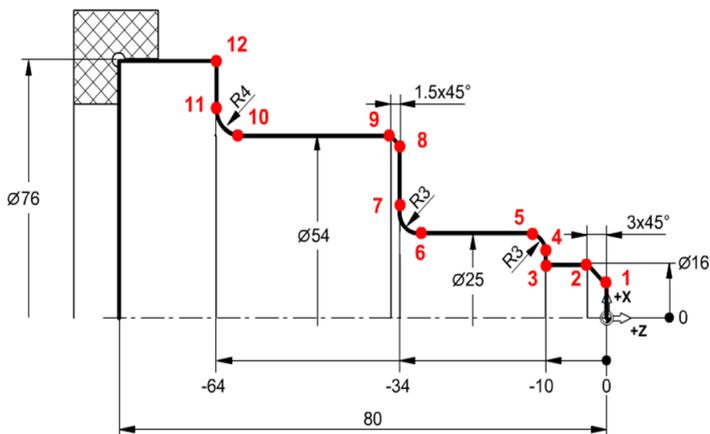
Эскиз детали «вал ступенчатый» [12]
